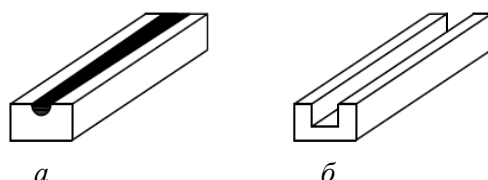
Фрезерование и распиловка брусков: *a* – бруски с ядровой гнилью; *b* – элементы углового профиля
